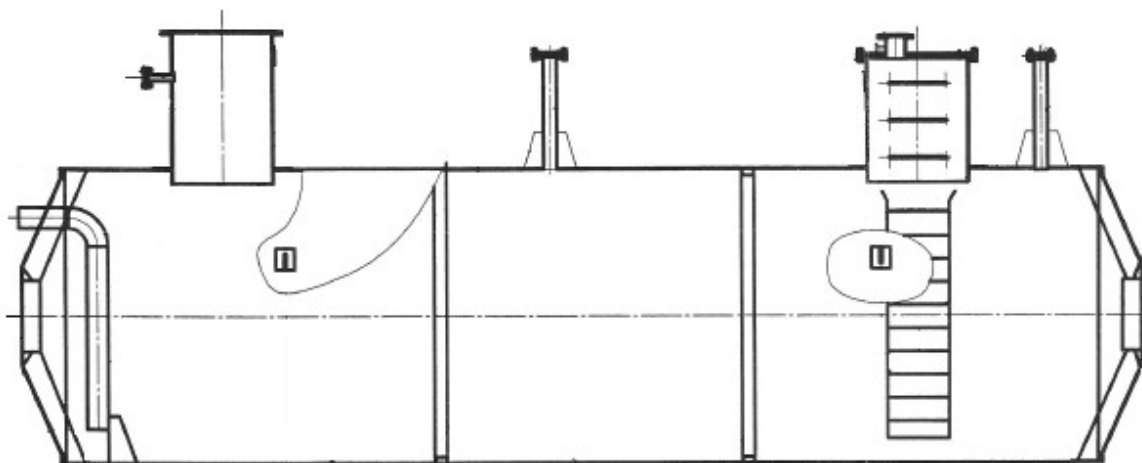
Общий вид эскиза резервуара РГС-16
